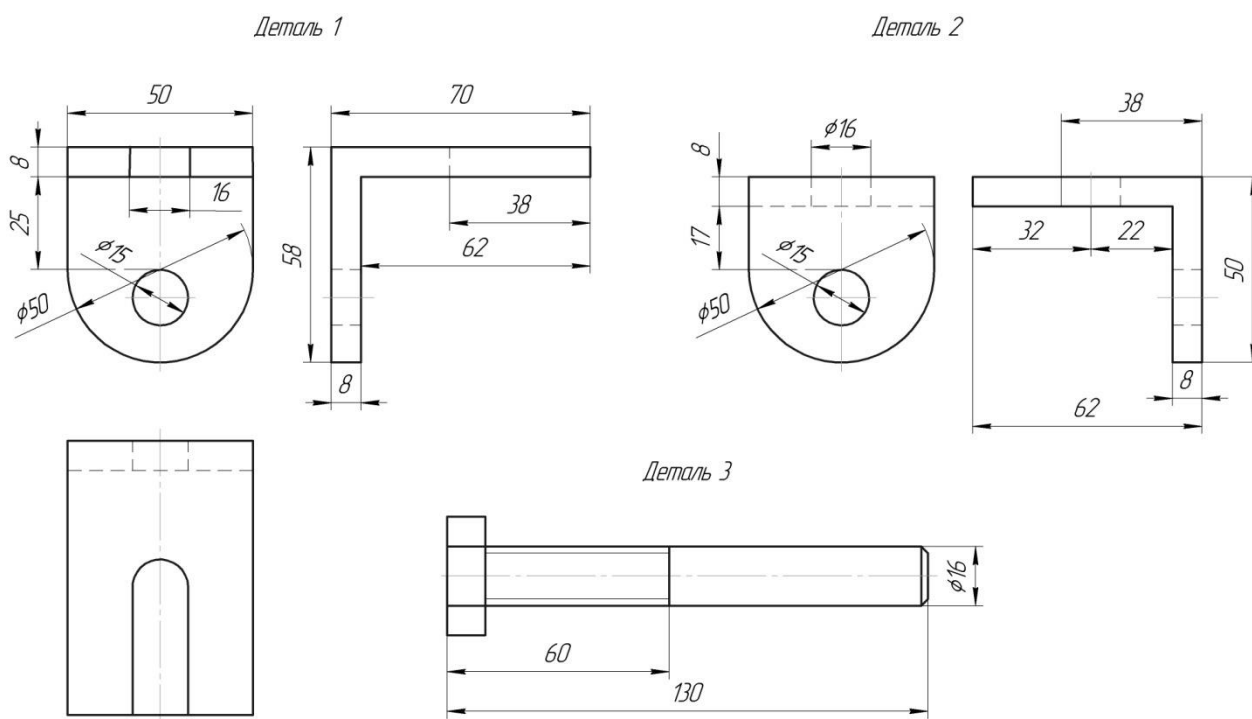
Эскиз деталей оснастки для растяжения крестообразных сварных соединений
